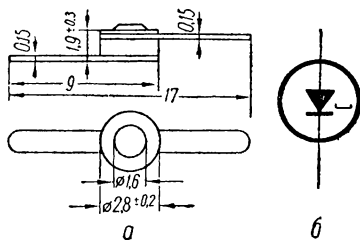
Туннельный диод: а — габаритный чертеж; б — условное обозначение.
